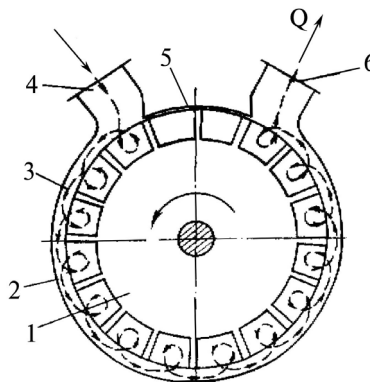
Принципіальна схема вихрового насоса: 1 – робоче колесо; 2 – корпус; 3 – кільцевий проточний канал; 4 – усмоктувальний патрубок; 5 – роздільна перемичка (ділянка); 6 – напірний патрубок.
